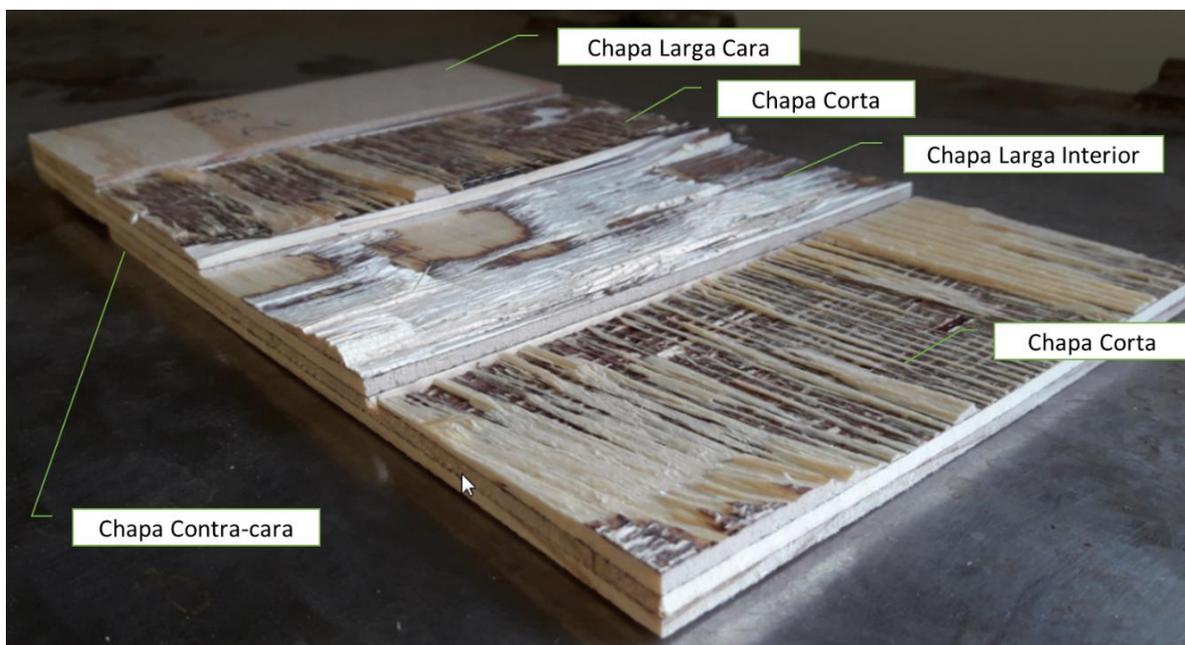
Muestra Distribución de chapas de un tablero contrachapado.
